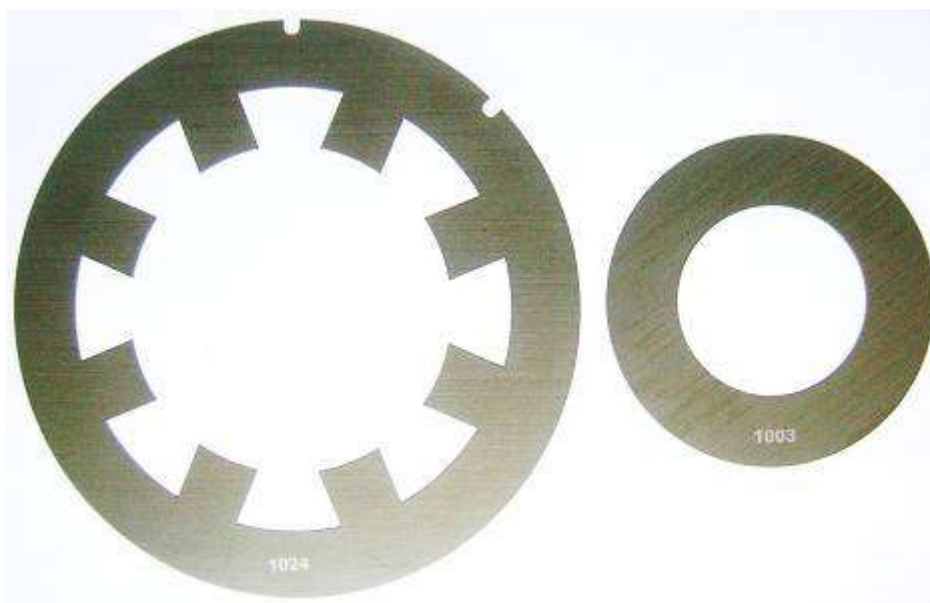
Пластины статора и ротора, изготовленные на станке лазерного раскроя LaserCut-6020
